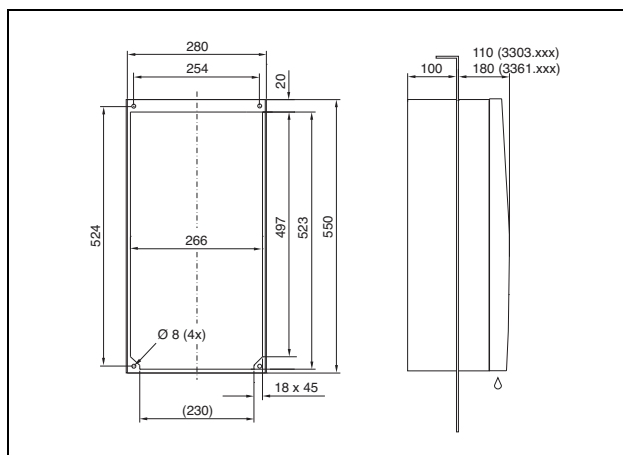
3303.xxx, 3361.xxx полутопленный монтаж
